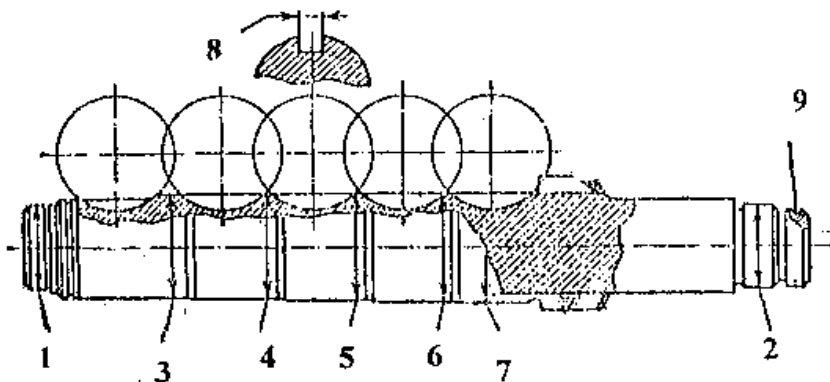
Промежуточный вал коробки передач ЗИЛ-130.
